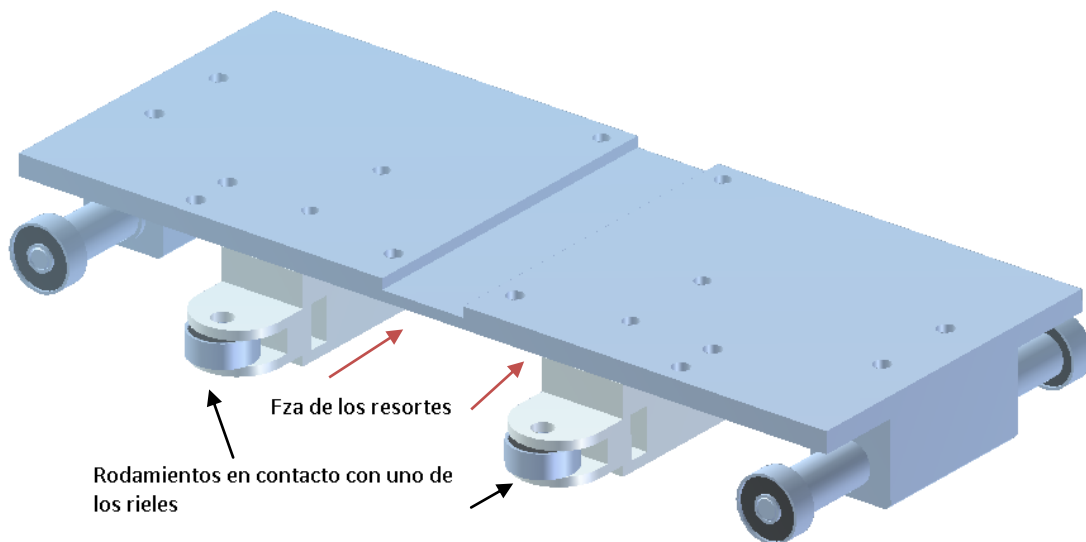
Ensamble del “carrito”, conformado por: placa base, camisa del eje, eje, rodamientos y compensador.
